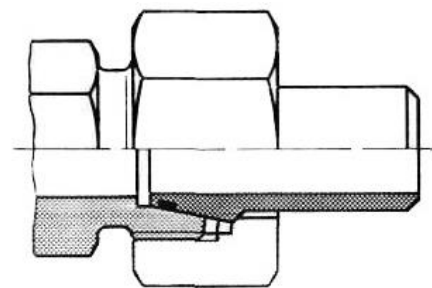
Різьбове з'єднання з конічним штуцером по DIN 3865 під зварку
